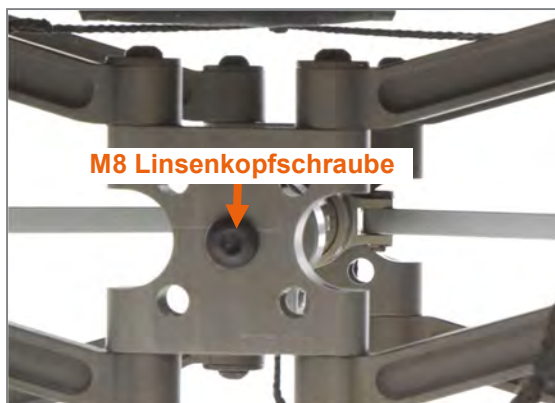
M8 Linsenkopfschraube, die das hintere Mittelteil des Faltmechanismus mit dem Zentralrohr verbindet (Rollstuhl von hinten)
